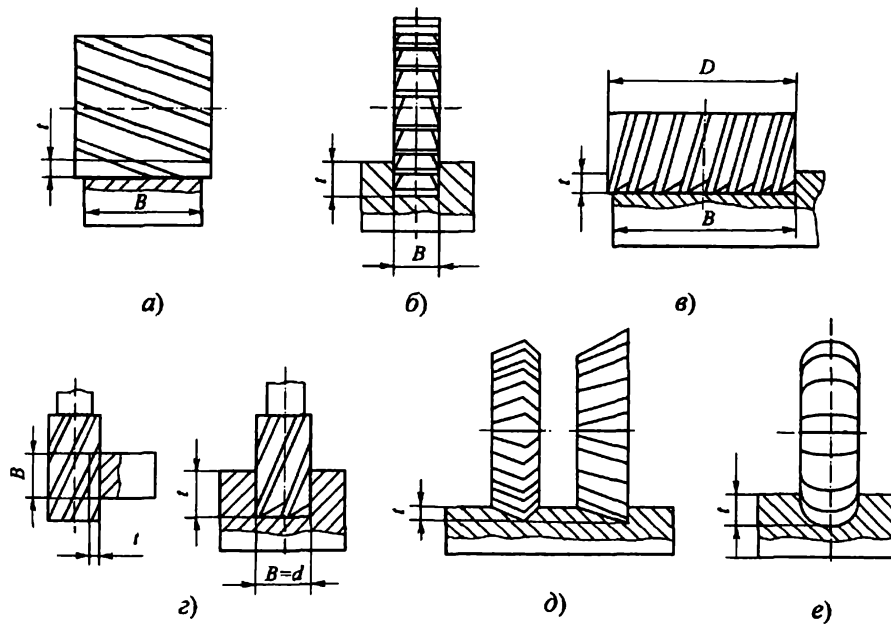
Типы фрез: *a* – цилиндрическая; *б* – дисковая; *в* – торцевая; *г* – концевая; *д* – угловая; *е* – фасонный
